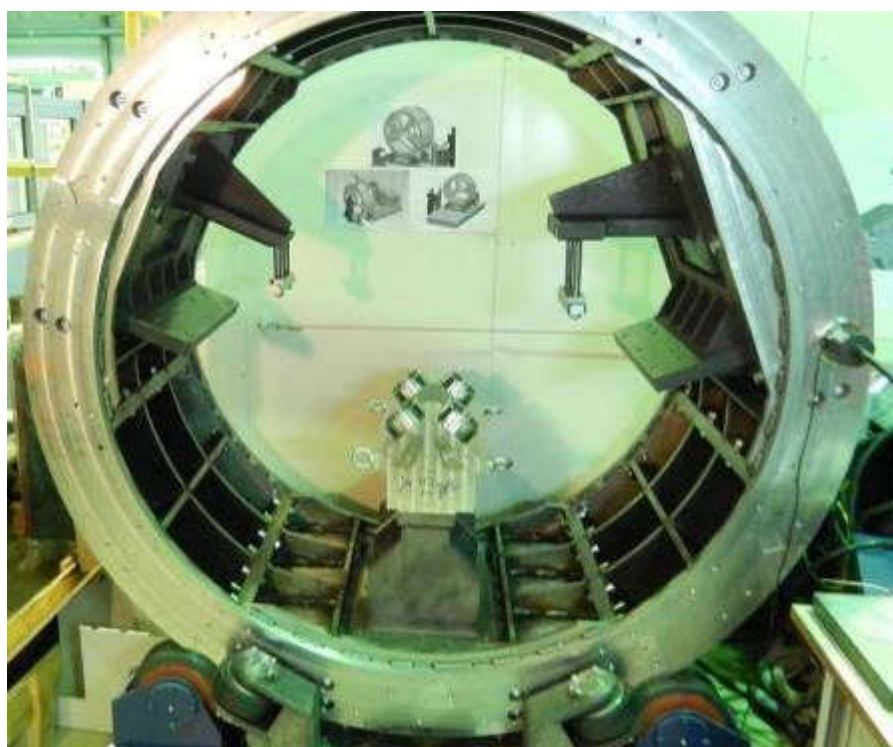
Оснастка для сборки и сварки СОК
